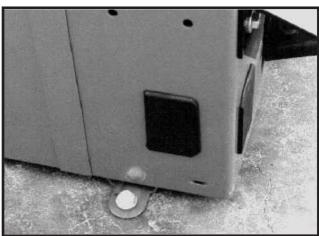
Fissaggio al suolo della macchina Fig.28 Fixation de la machine au plancher.
